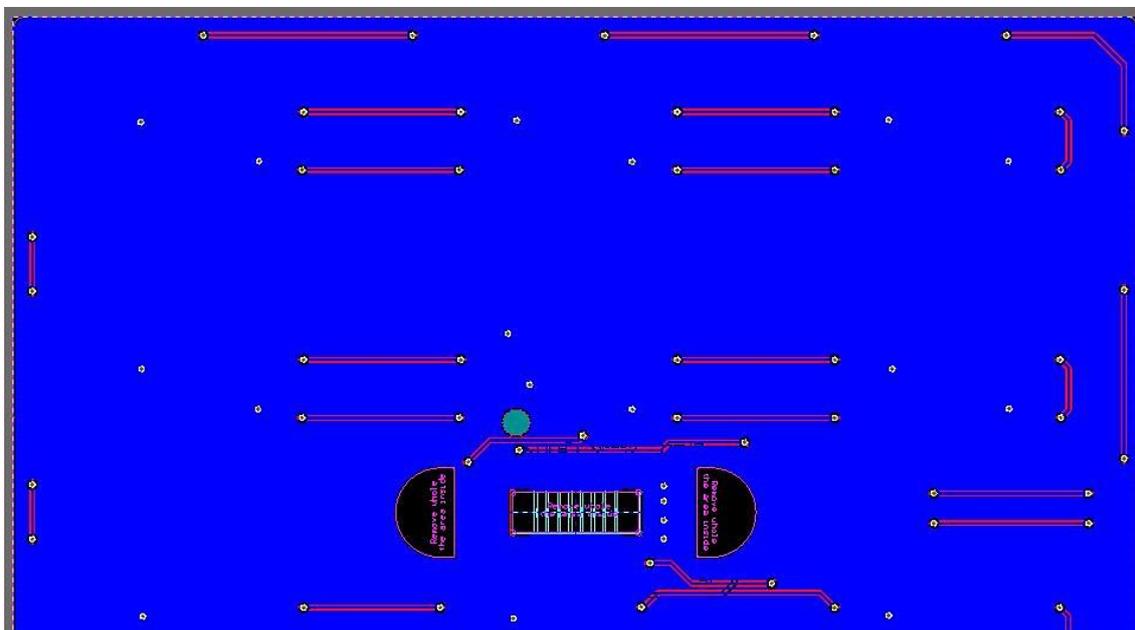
Capa inferior del diseño final PCB Pixel Blanco.
